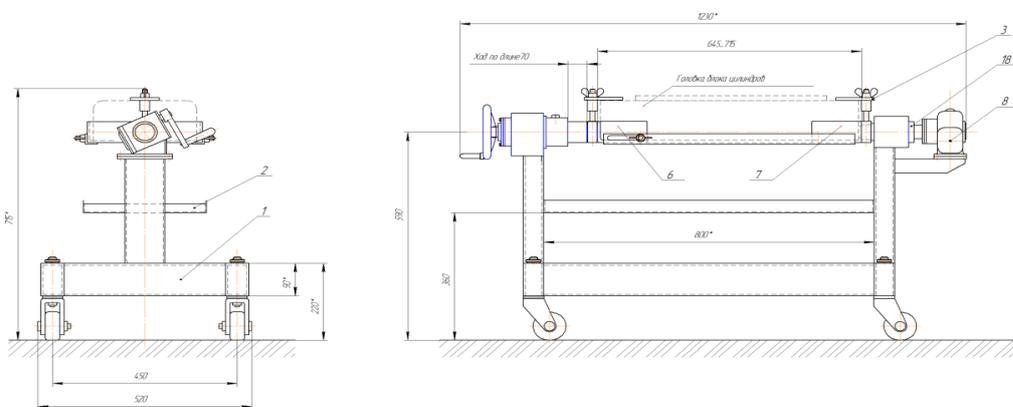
Стенд для ремонта головок блоков цилиндров
